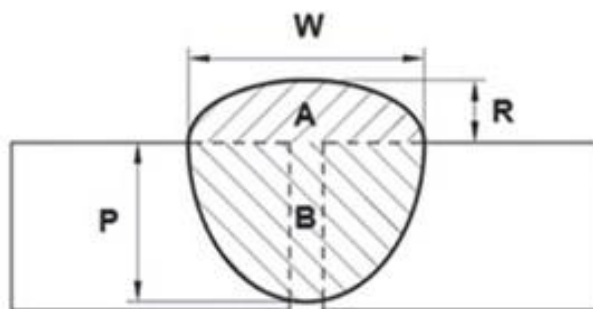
Desenho esquemático das dimensões avaliadas: W - largura, R - reforço e P - penetração.
